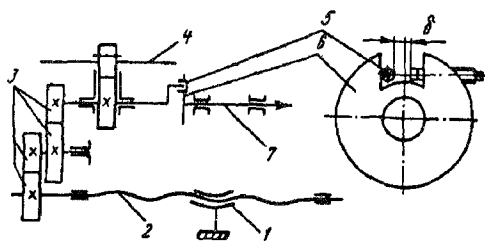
Схема компенсации зазора в зубчатых и винтовой передачах механизма подачи резьбошлифовального станка
